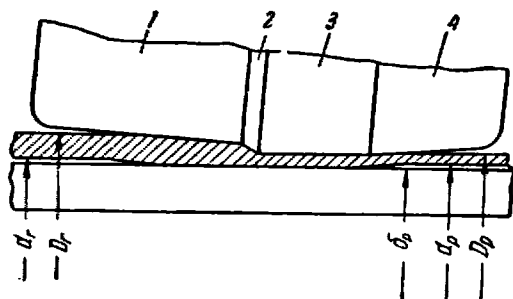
Схема прокатки в чистой клетке трехвалкового стана
